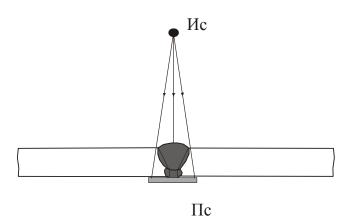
Схема просвечивания сварного соединения
